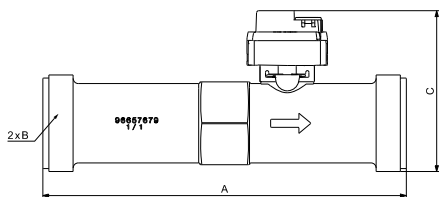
Abmessungen des Sensors VFS 20-400 l/min (ohne Adapter)
